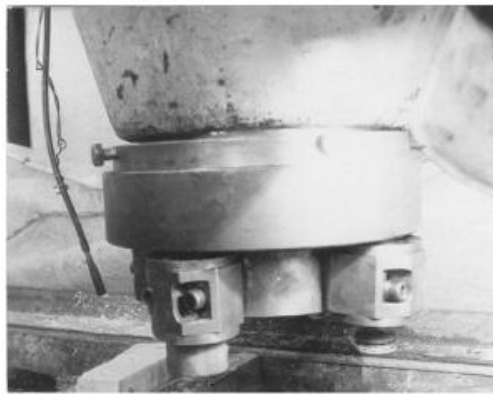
Комбінована фрезерно-шліфувальна головка [10]
